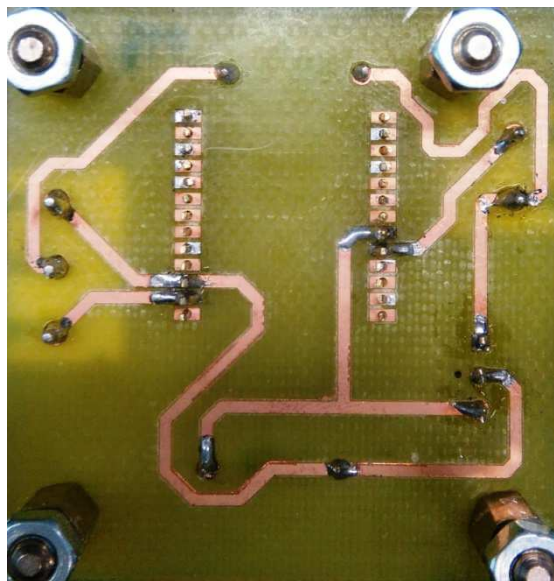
PARTE IMPRESA DE LA PCB DEL MÓDULO PARA EL SENSADO MEDIANTE BLE
